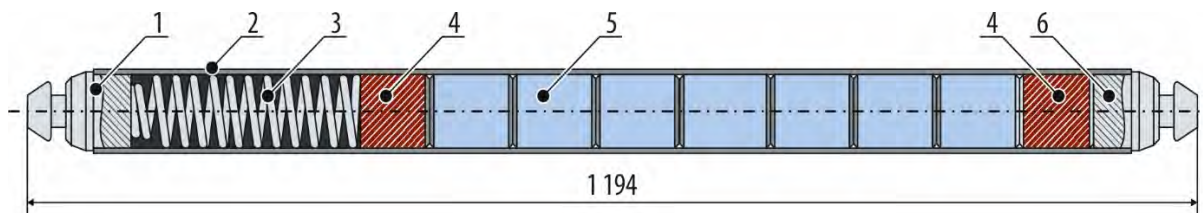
Общий вид твэла специального облучательного устройства:
